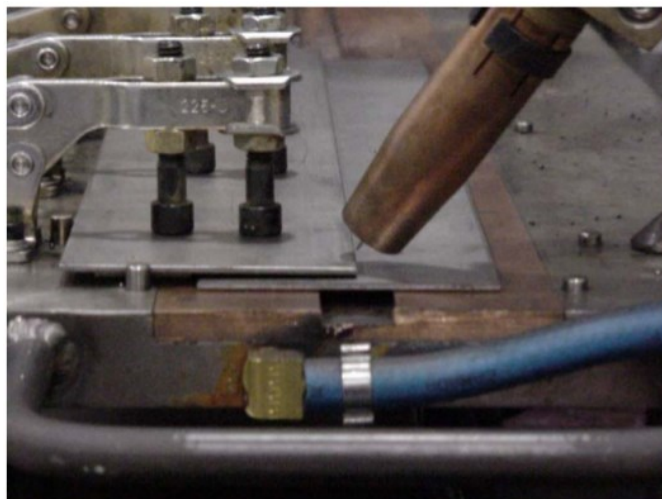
Soldagem MIG/MAG Pulsado CA de junta sobreposta formada por chapas de aço ao carbono.
